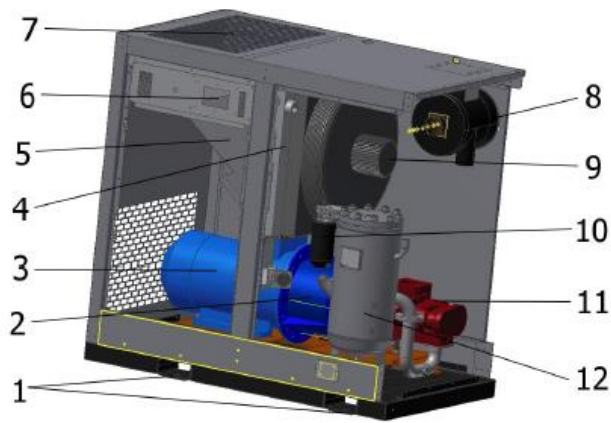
Состав установки: 1 – отверстия под захваты вилочного погрузчика; 2 – проставка муфты; 3 – электродвигатель приводной; 4 – блок охлаждения; 5 – короб направляющий; 6 – панель управления; 7 – сетка выхода воздуха; 8 – воздухоочиститель; 9 – электрический вентилятор; 10 – фильтр масляный; 11 – компрессор; 12 – сепаратор
